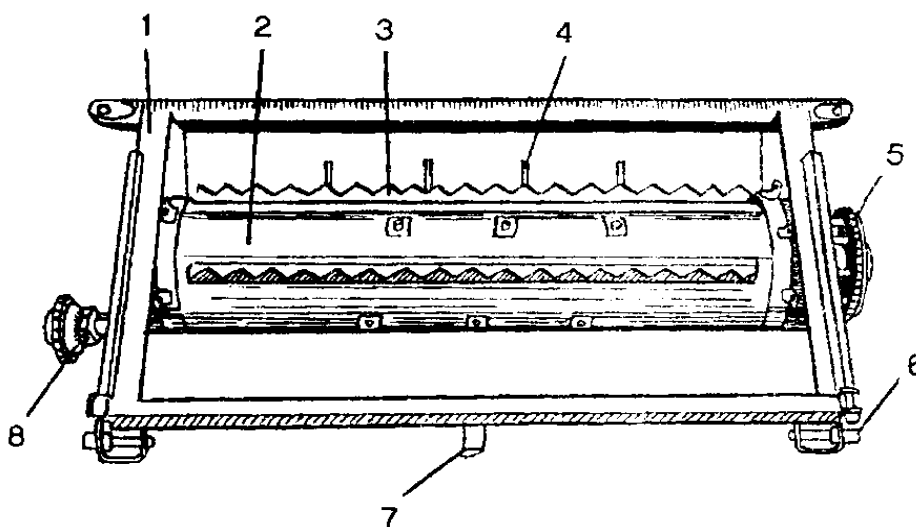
Проставка: 1 – корпус; 2 – битер; 3 – гребенка; 4 – палец; 5 – блок звездочек; 6 – ролик; 7 – шарнир; 8 – контрпривод
